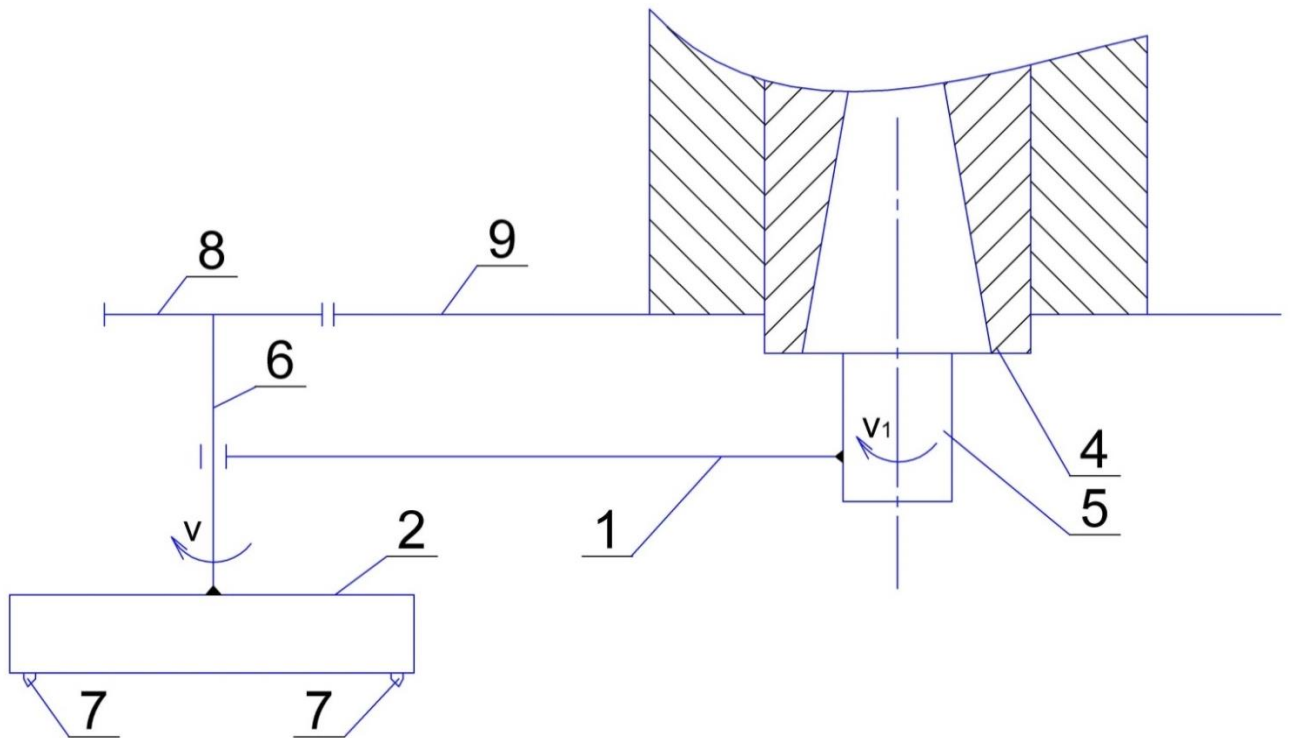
Схема способу плоского фрезерування широких площин
